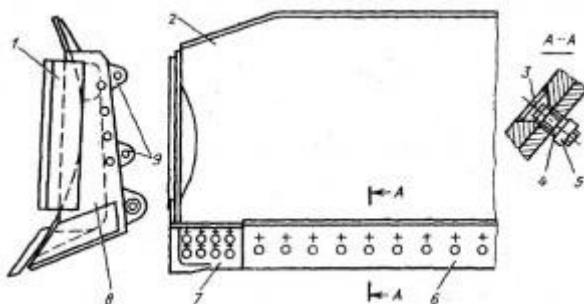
Отвал бульдозера ДЗ-54:1 — вертикальные ножи; 2 — лобовой лист; 3, 4, 5 — болты, шайбы, гайки; б — основной нож; 7— боковые ножи; 8— боковые щеки; 9 — кронштейн для крепления отвала
